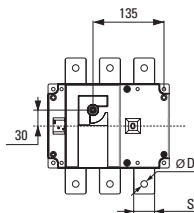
г – Монтажные размеры при установке на дверцу шкафа для рубильников 400-630 А
